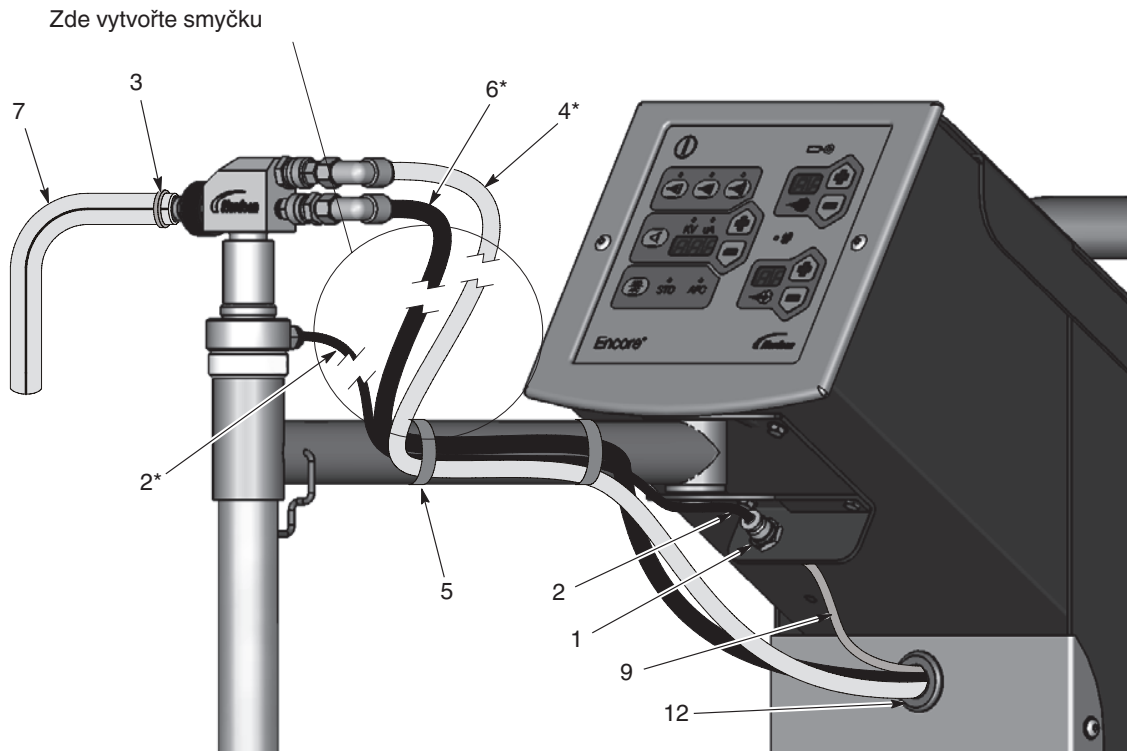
Instalace sběrné trubice a čerpadla pro pistolí Encore LT
